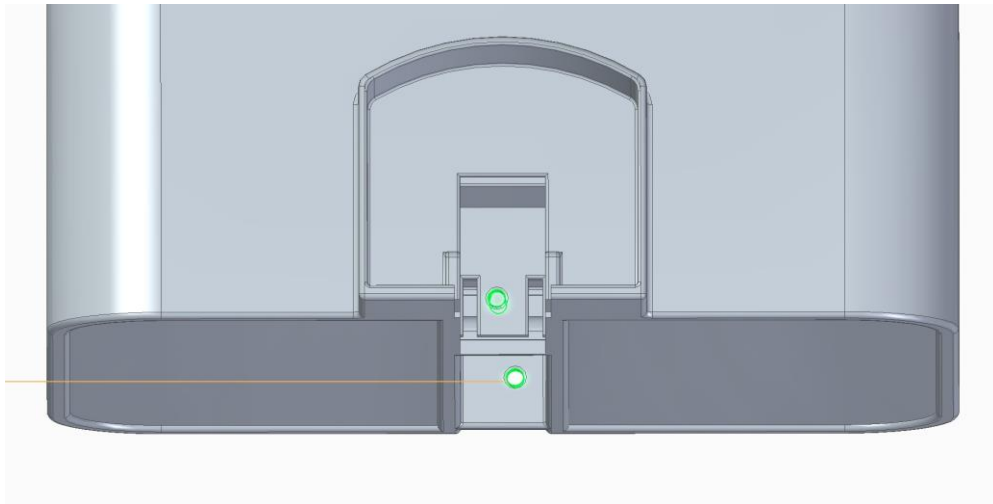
Sistema de varillas para la apertura de la tapa - vista anterior
